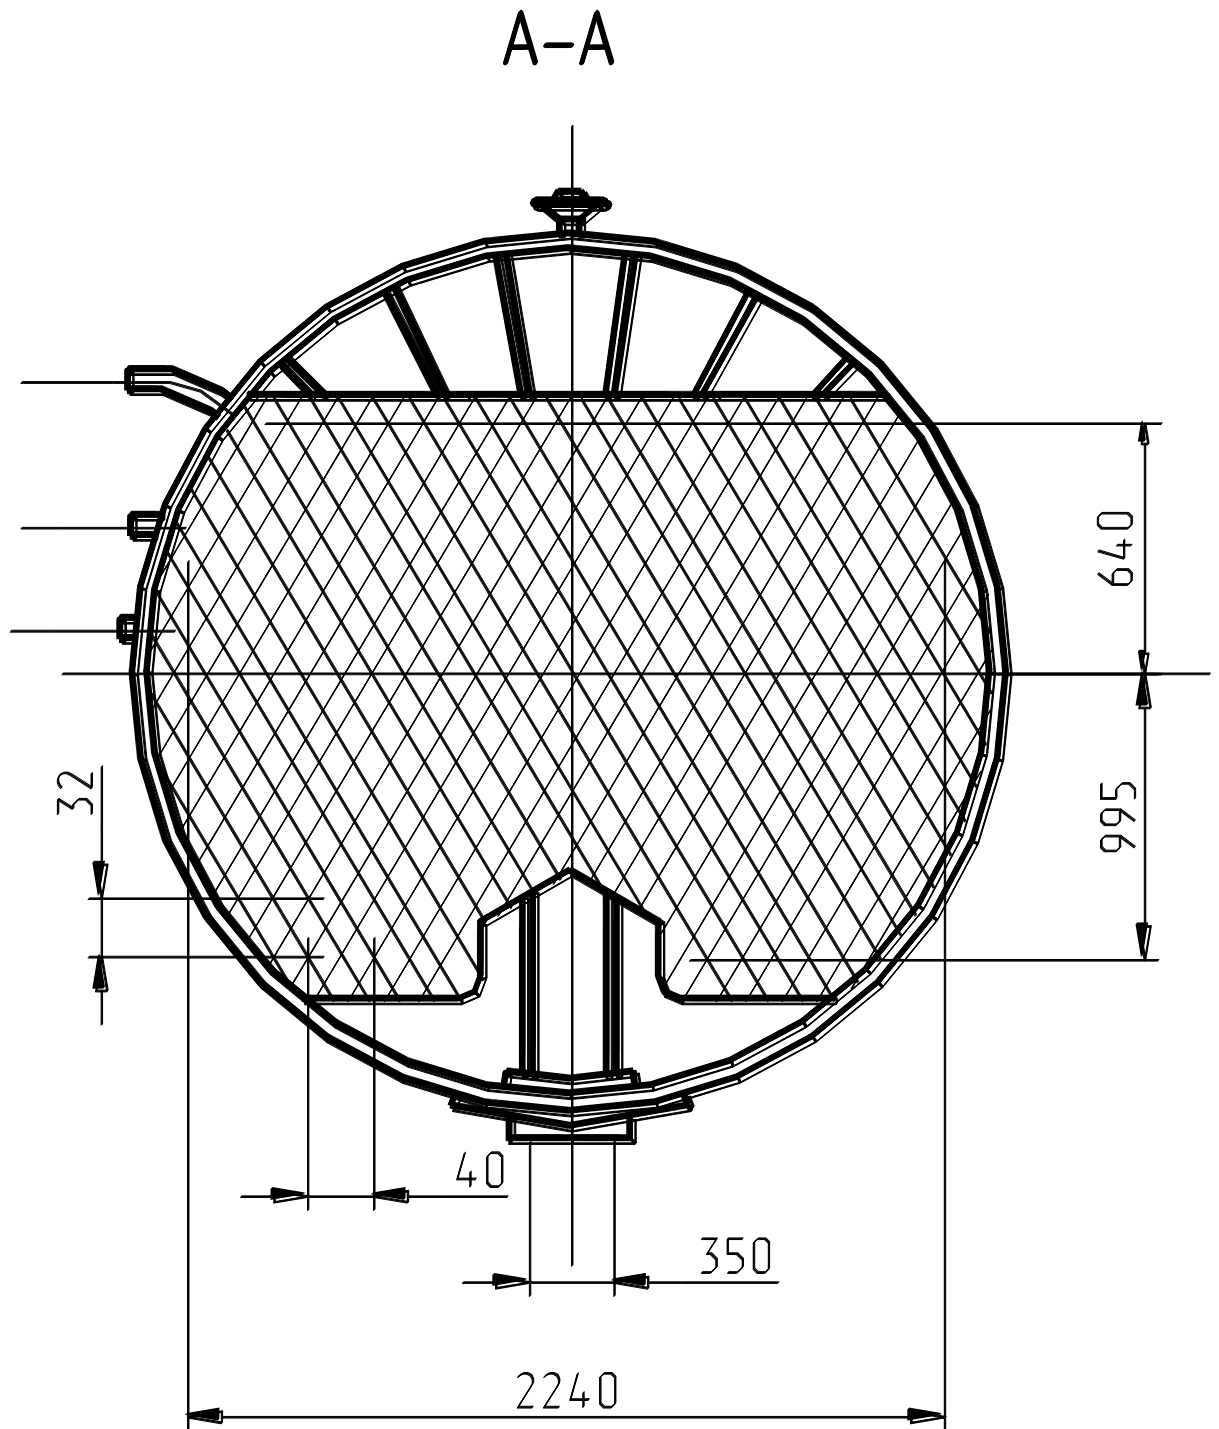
Разрез А-А корпуса барабана парового котла
